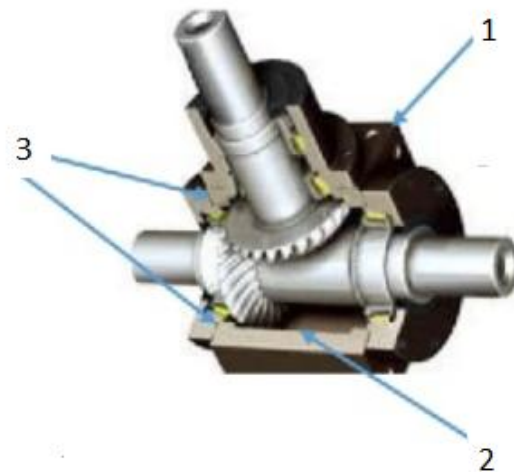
Редуктор с уплотнительными и изнашивающимися поверхностями
